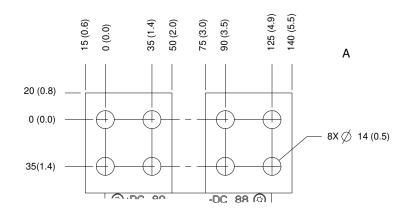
Dimensions des bornes de répartition de la charge/régén. E3h (vues latérales)
